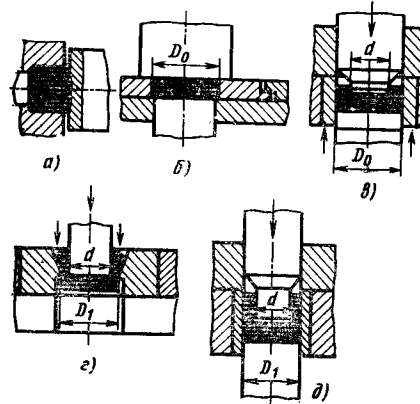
Технологические переходы штамповки корпуса карданного подшипника: а — отрезка и высадка на автомате; б — осадка в кольце; в — холодное выдавливание; г — вытяжка с утонением; д — калибровка
